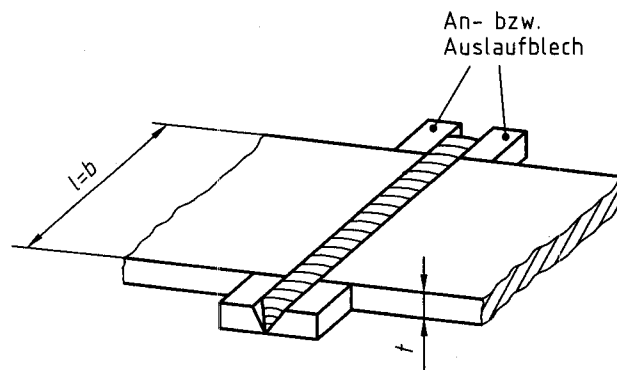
Stumpfnäht mit An- bzw. Auslaufblechen
